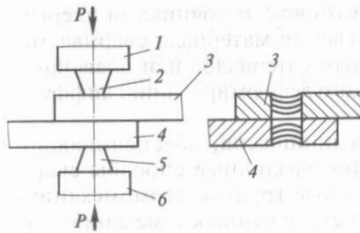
Схема холодной сварки: 1, 6 — опорные части; 2, 5 — опорные выступы; 3, 4 — свариваемые заготовки
